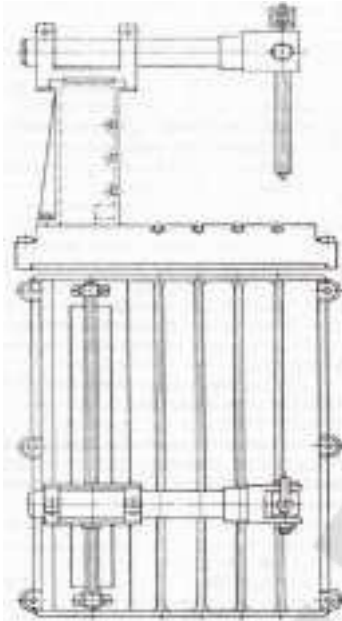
Универсальный стенд для испытания на жесткость
